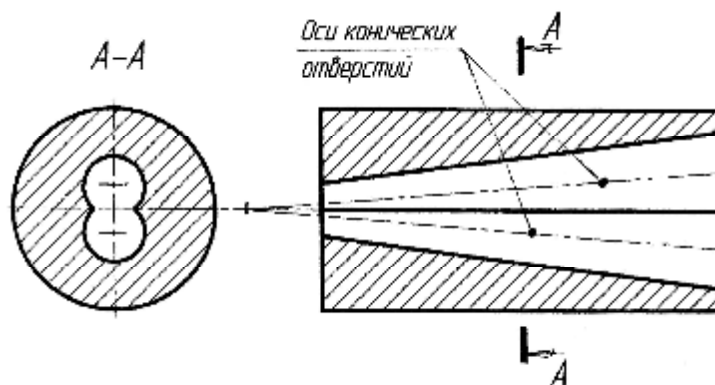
Корпус цельного двухчервячного конического экструдера
